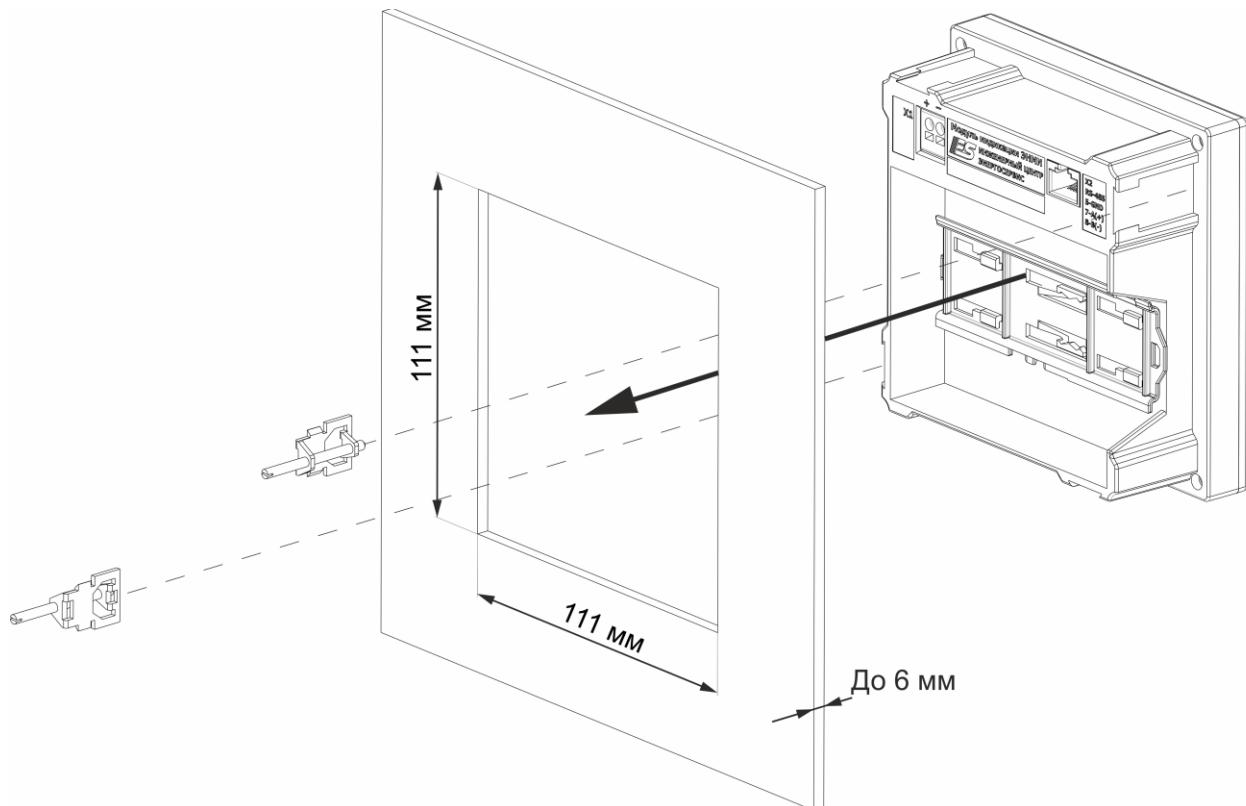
Схема установки и крепления модуля индикации ЭНМИ-X-24-2 в щит.
